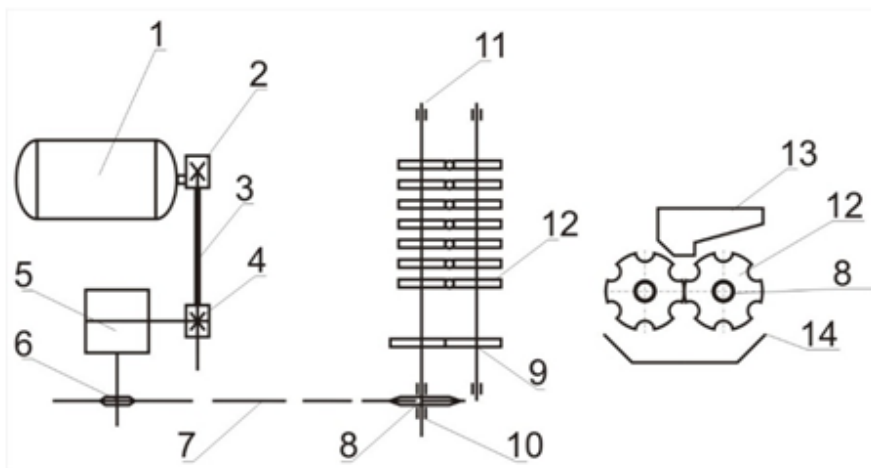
Кинематическая схема механизма для колки грецкого ореха: 1- электродвигатель; 2, 4 – ведущий и ведомый шкивы; 3 – ременная передача; 5 – червячный редуктор; 6 – ведущая звездочка; 7 – цепь для привода механизма для колки грецкого ореха; 8 – ведомая звездочка с ведущим валом для колки грецкого ореха; 9 – открытая зубчатая передача; 10, 11 – подшипниковые опоры для привода валов для колки грецкого ореха; 12 – противоположные диски с валом, 13 – загрузочный бункер; 14 – приемный бункер.
